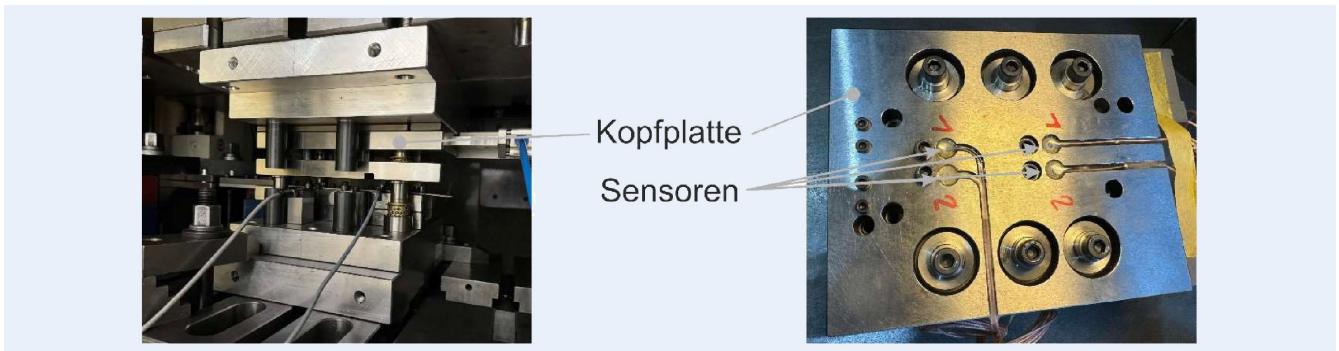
Werkzeug mit Kraftsensoren in der Kopfplatte. Grafik: Fraunhofer IWU
